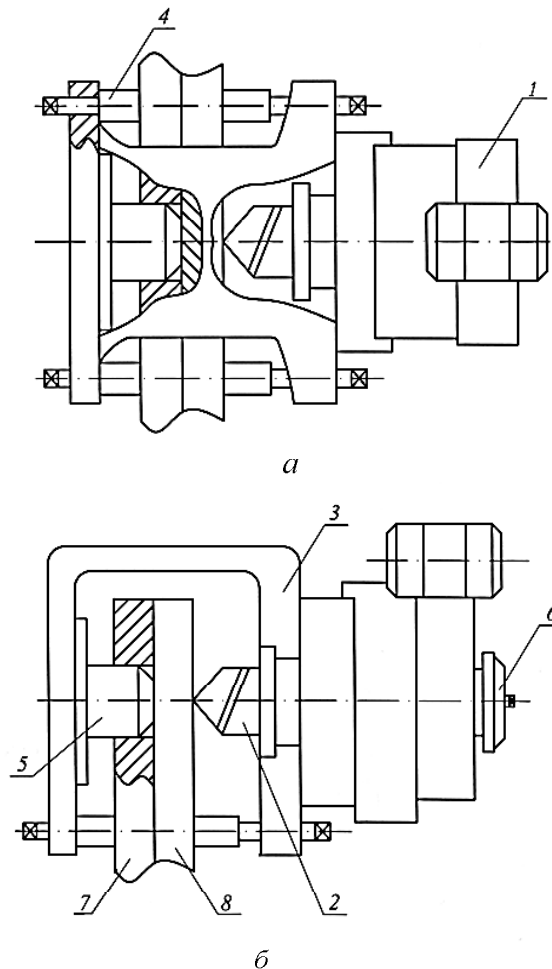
Станок для сверления и растачивания отверстий в крупногабаритных фланцевых соединениях: а – вид сбоку; б – вид сверху:
